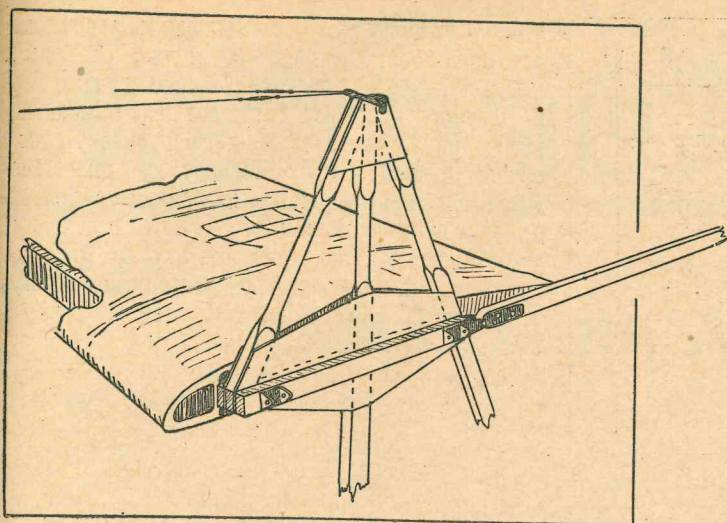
Конструкция к бана и крепление крыльев к ферме
